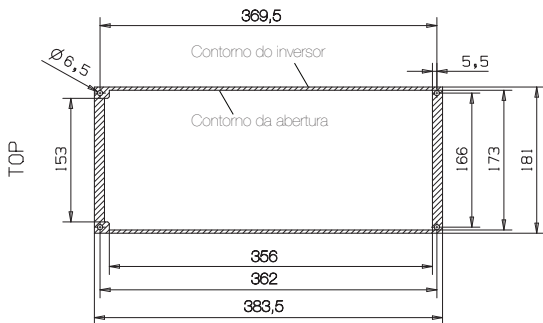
Dimensões do recorte para montagem com flange do MR4 ao MR6 (unidade: mm)
